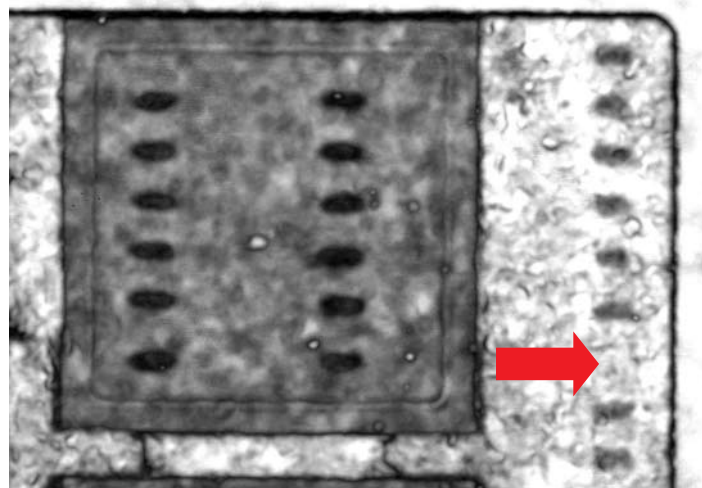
Исследование сварных соединений с помощью ультразвукового сканера (продолговатые отпечатки сварных соединений на кристалле (слева) и подложке (справа) говорят о качестве диффузии металлов в месте сварки; стрелкой показано дефектное соединение)
